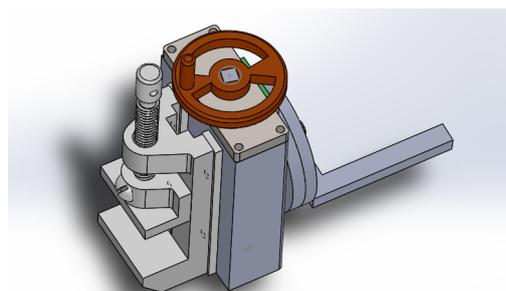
Tampak Depan Desain *Jig And Fixture Attachment
